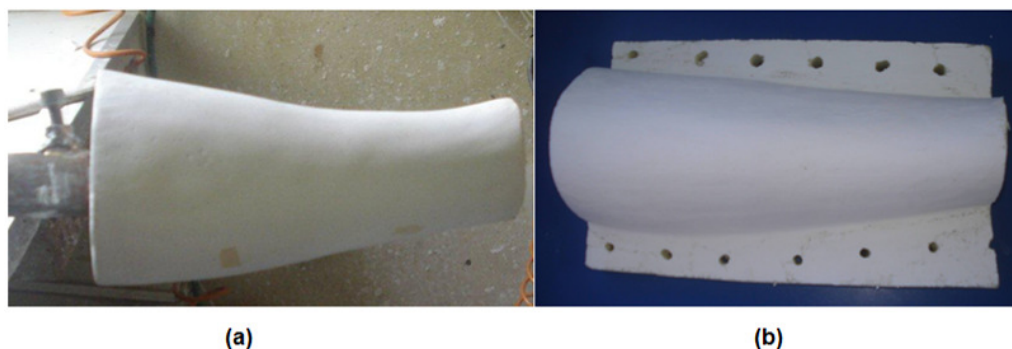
Suporte do molde (a) em gesso e conectado ao aparelho de vácuo. (b) em P.U furado para ser fixado para termoformagem
